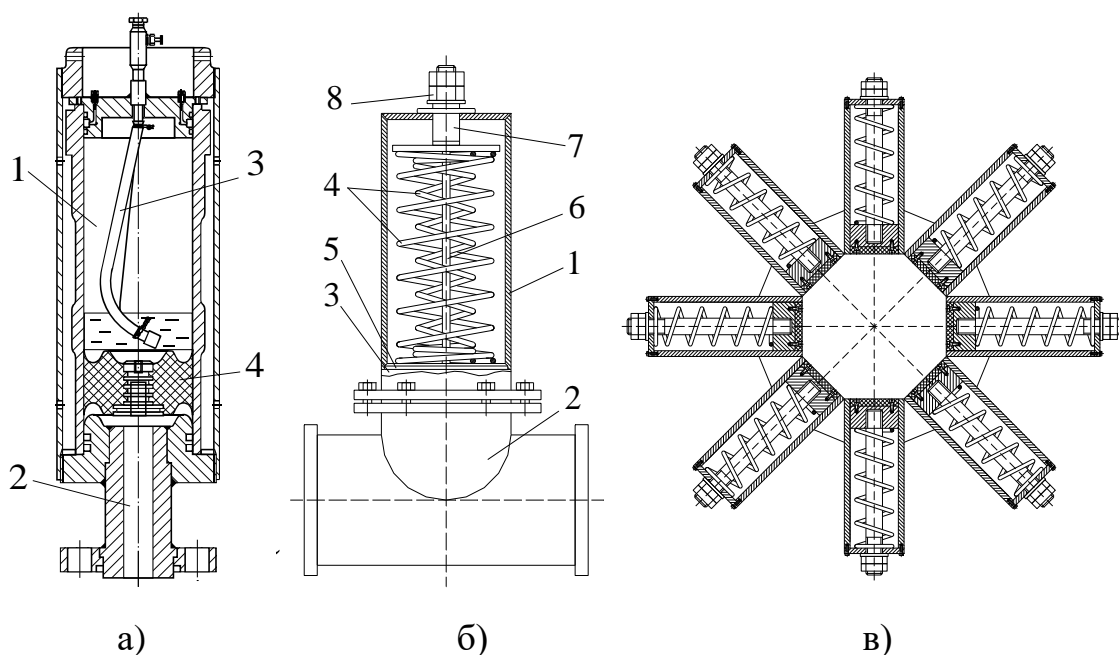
Компенсатори поршневі: а – пневмокомпенсатор СевКавНДІ; б – пружинного типу; в – кільцевий поршневий блок компенсатора
